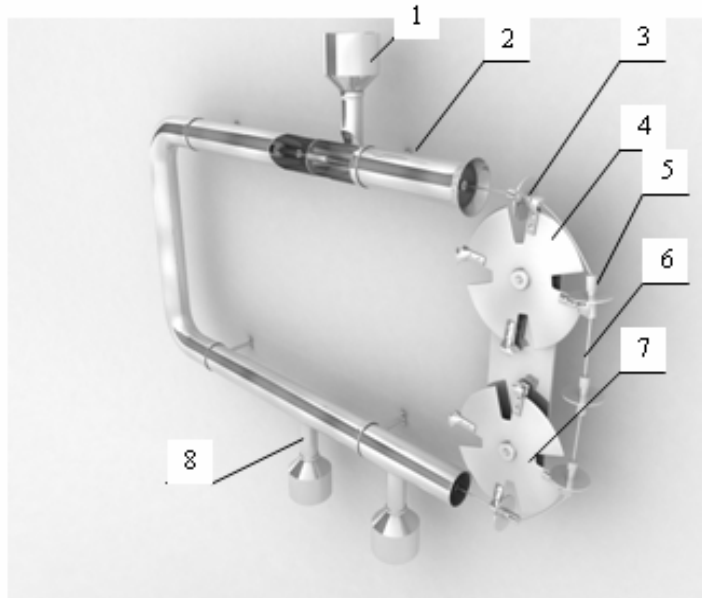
Установа трубчастого гнучкого канатного конвеєра: 1-завантажувальний бункер; 2-труба; 3- робочий орган; 4-привідна зірочка; 5-кріпильна втулка; 6-канат; направляюча зірочка; 8-розвантажувальний бункер.
